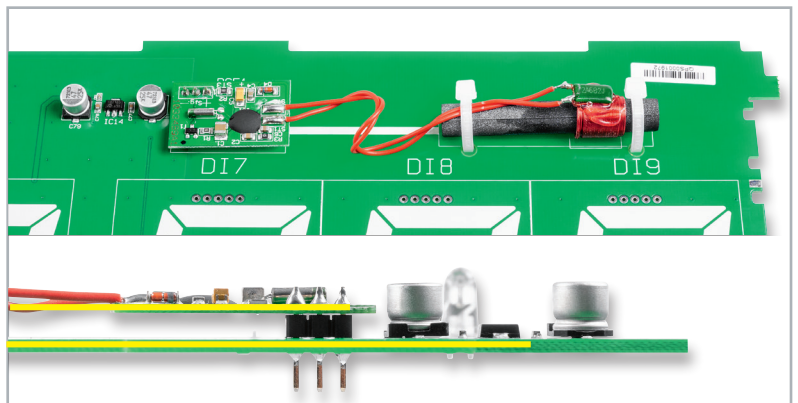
Die Bestückung und Montage des DCF-77-Empfängers. Dieser ist exakt parallel zur Hauptplatine einzulöten.
